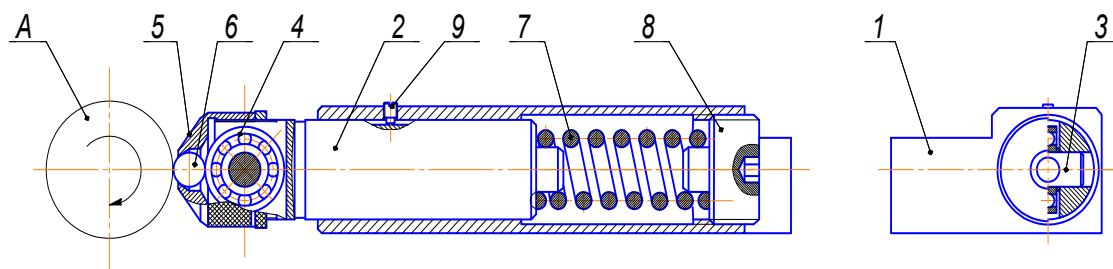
Конструкція кулькового інструмента для обкочення зовнішніх циліндричних поверхонь
